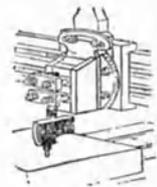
Ausrichten d. Werkstückes auf der Tischhobelmaschine.
